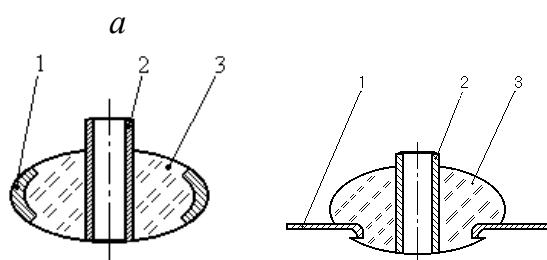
Конструкции гермовыводов для пайки (а) и сварки (б),
